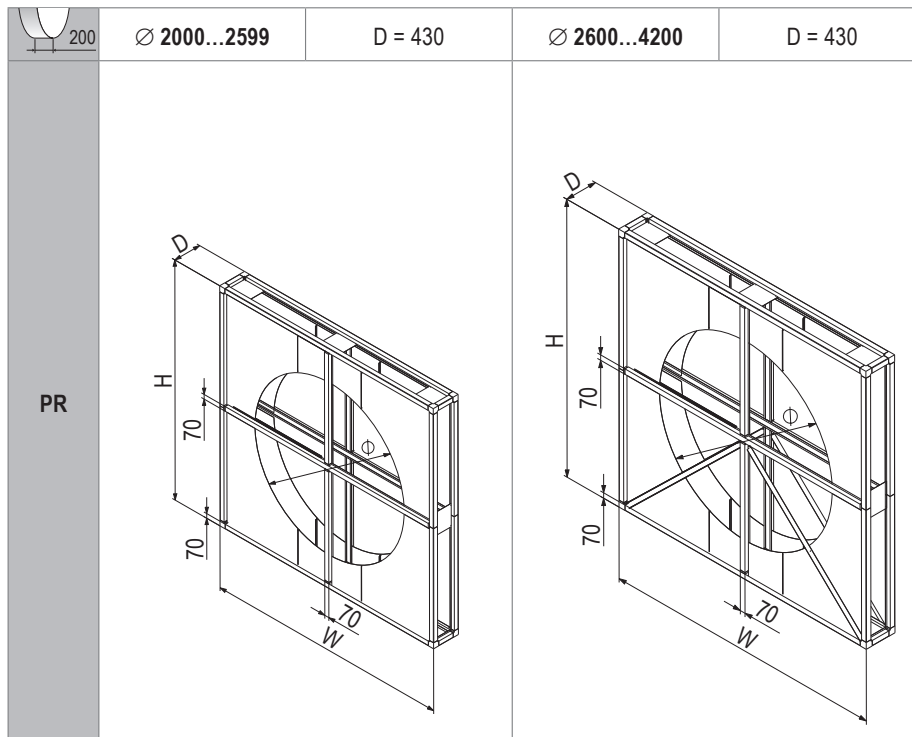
Massblatt für PR Gehäuse (Abmessungen in mm)
